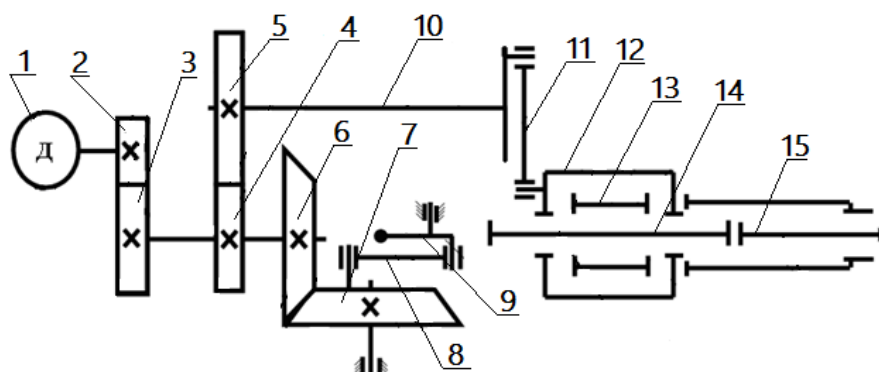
Кинематическая схема перфоратора с ударно-поворотным механизмом
